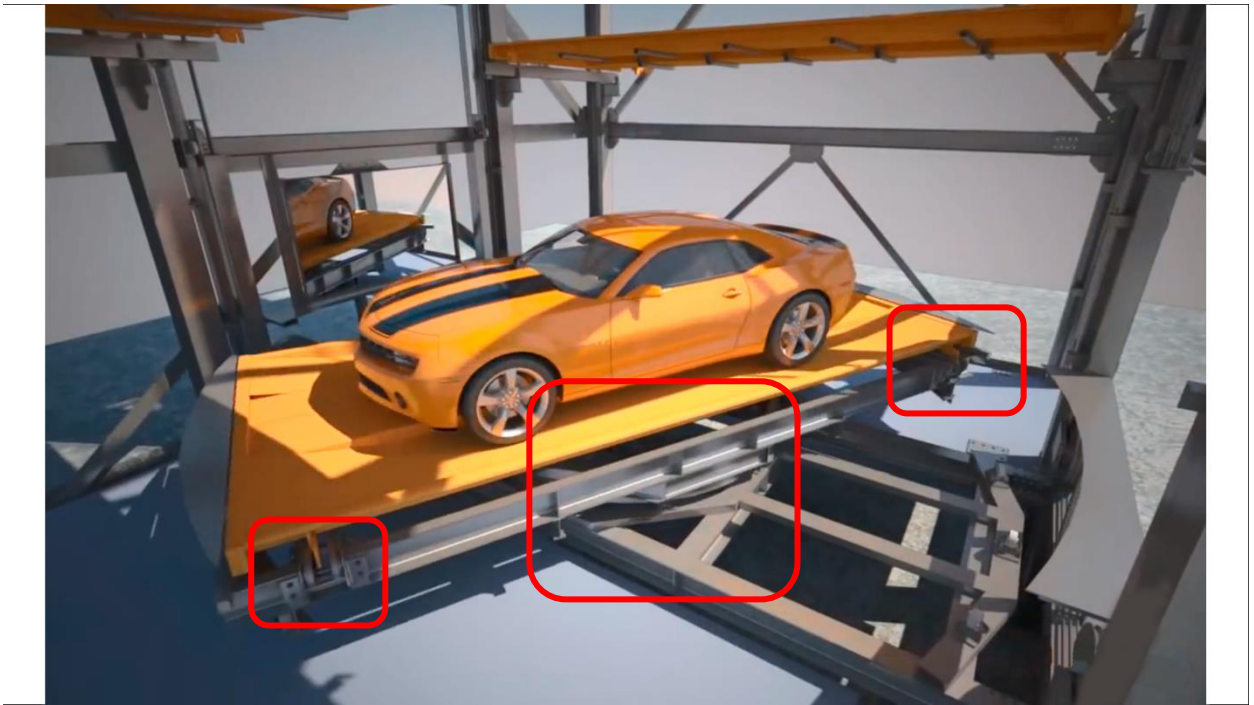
Поворотний механізм, в процесі розвороту. Штовхальний механізм
